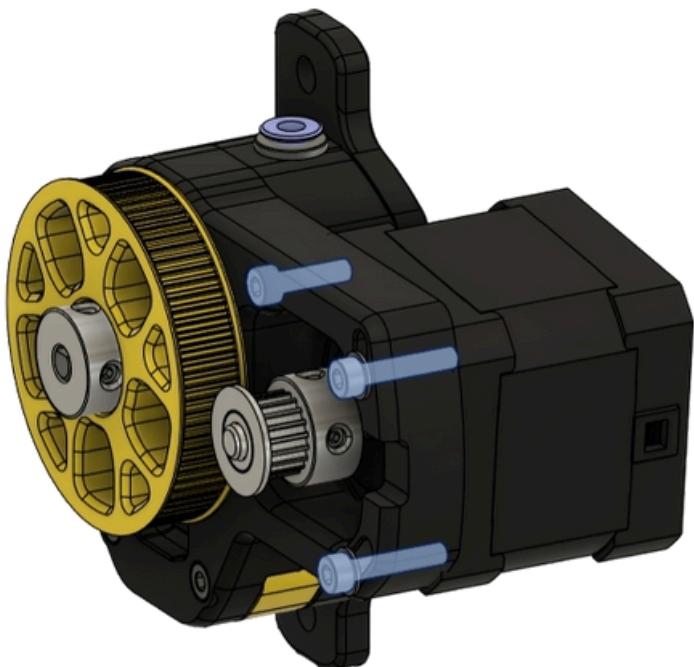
Disposición del motor en el ensamblaje del extrusor.
